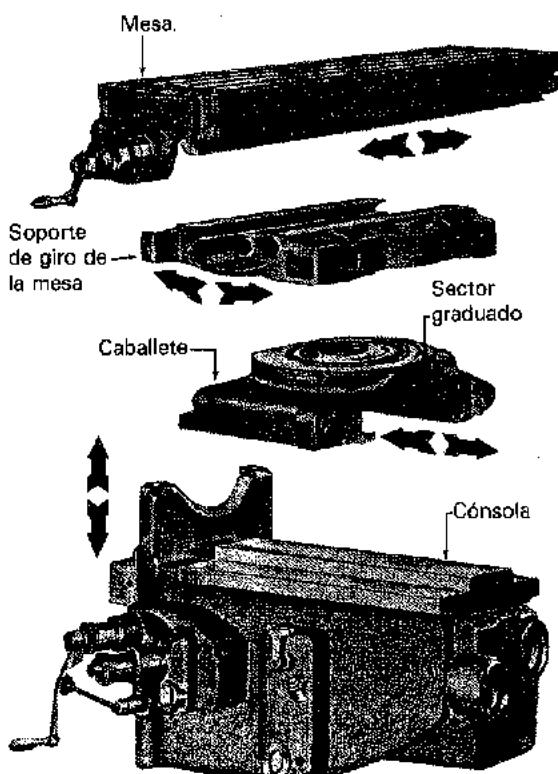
Elementos mecánicos de la fresadora universal del tipo de columna y cartela (Cincinnati Milling Machine Co.)
